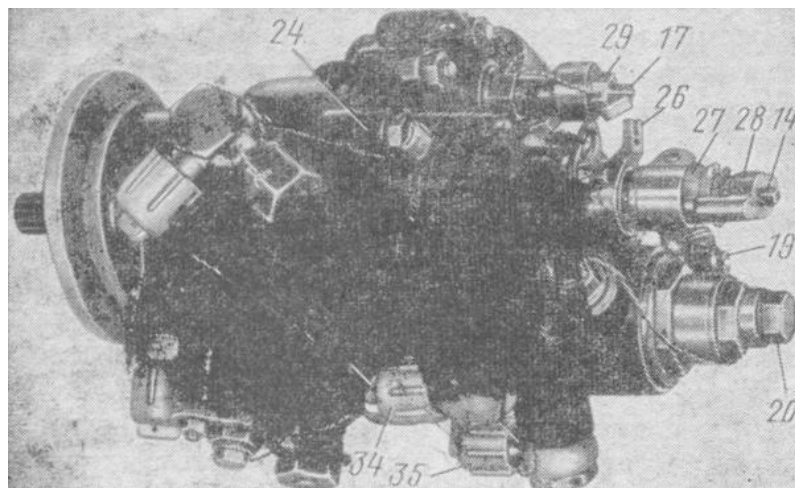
Регулятор числа оборотов РО-40ВА (внешний вид):
